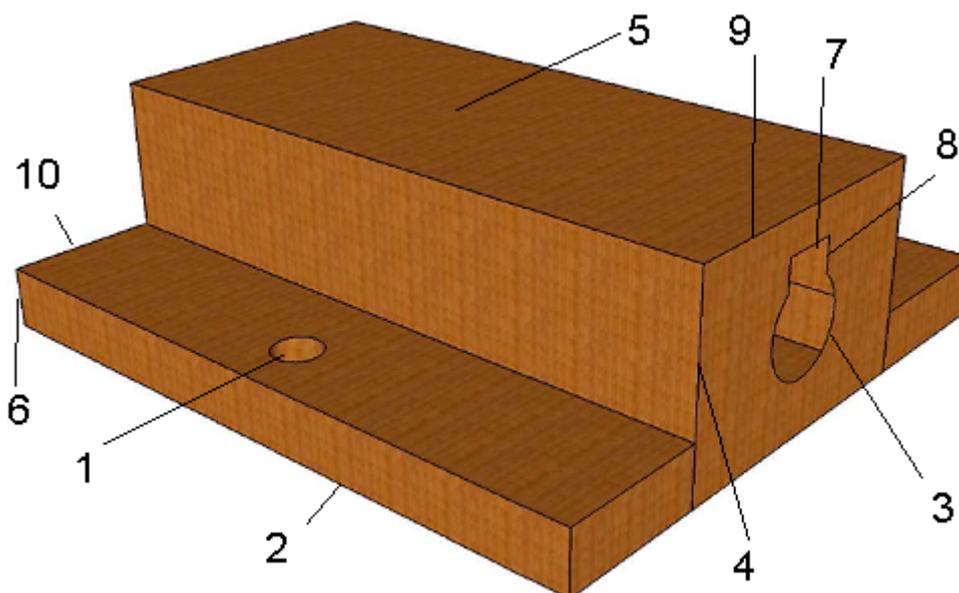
Desenho esquemático do F01 – Suporte para Colagem.
